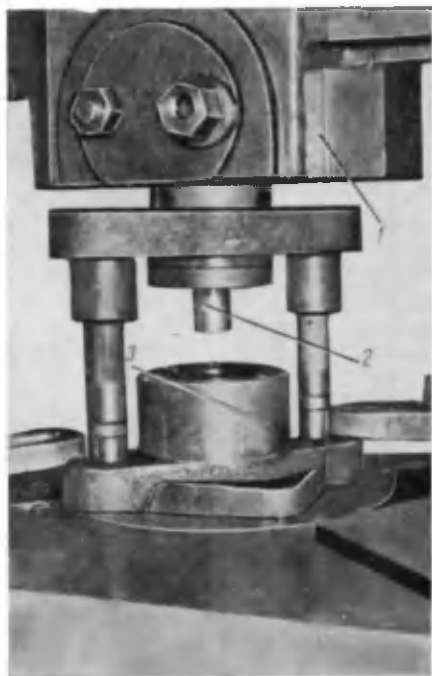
Рабочая часть прессы и штампа для штамповки диафрагм ртутно-цинковых элементов:
